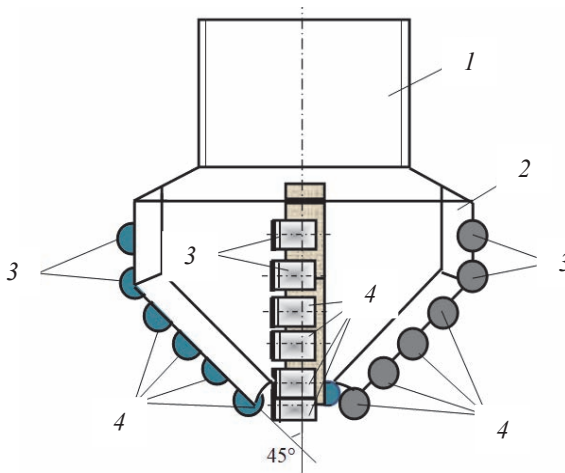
Долото с вращающимися резцами PDC: 1 – корпус с резьбой; 2 – матрица; 3 и 4 – вращающиеся резцы
